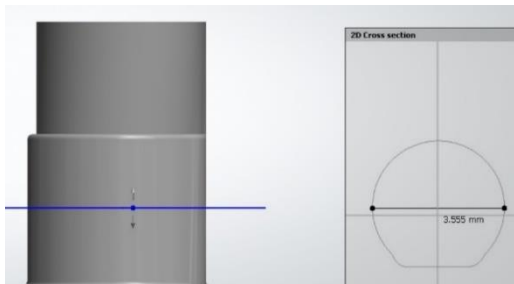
Dimensión inferior de la camisa diseñada en CAD
